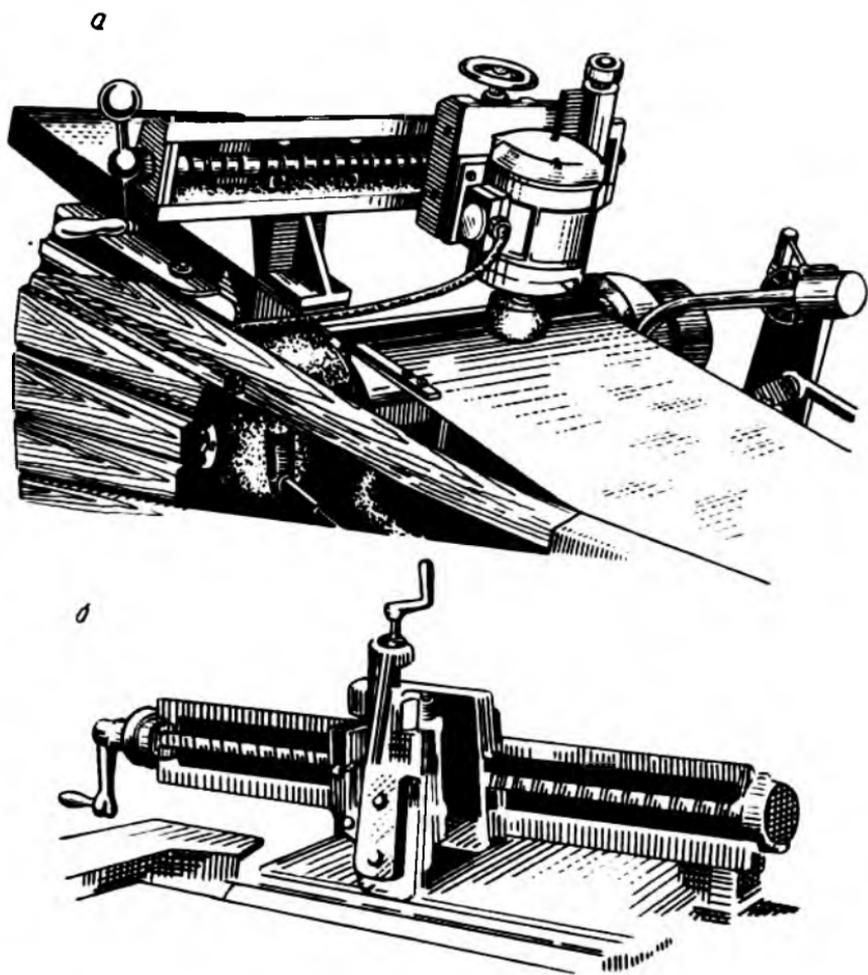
Приспособления для заточки и фугования ножей на валу:
